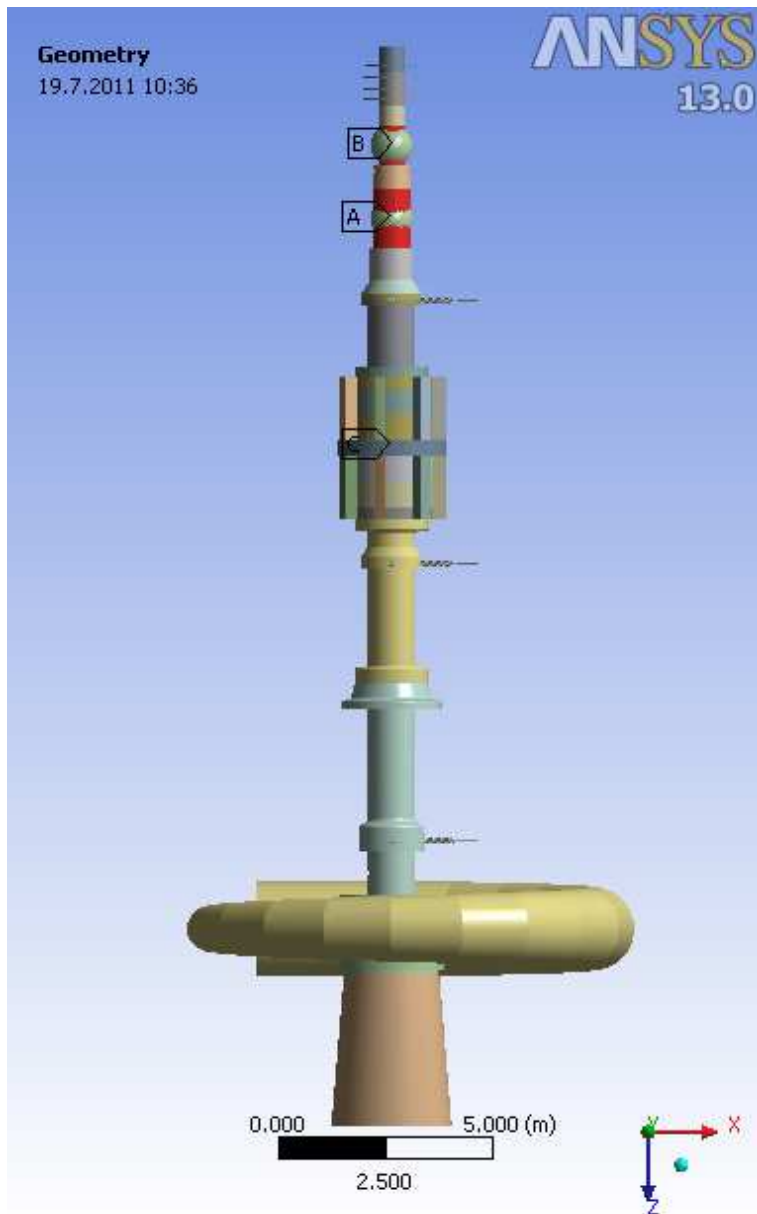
Schéma rotoru soustrojí PVE Dlouhé Stráně
